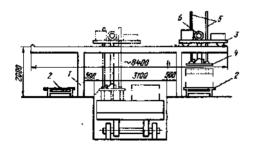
Схема садочного манипулятора: 1 – портал; 2 – конвейер; 3 – приводная тележка; 4 – захватное устройство; 5 – направляющие штанги; 6 – электроталь
